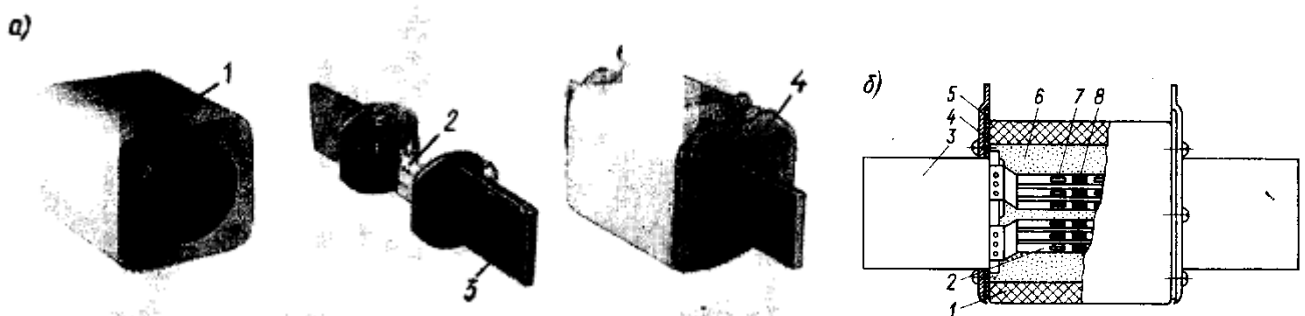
Запобіжники серії ПН-2: а - загальний вид і деталі; б - розріз
